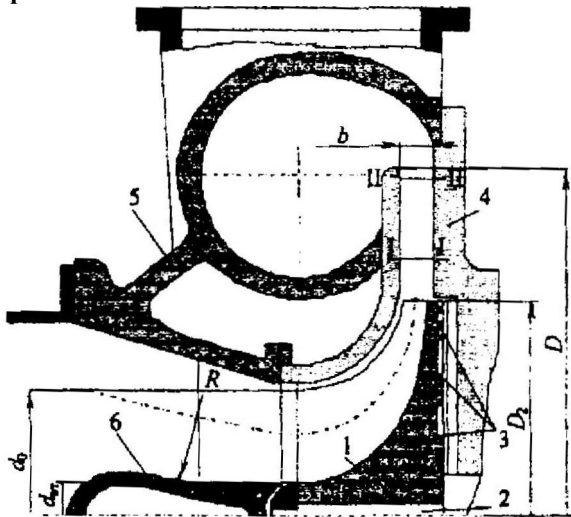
Розрахункова конструкція проточної частини компресорного ступеня: 1- робоче колесо; 2- вал; 3 - лабиринтоне ущільнення; 4- дифузор; 5-равлик; 6-всмоктуючий патрубков
